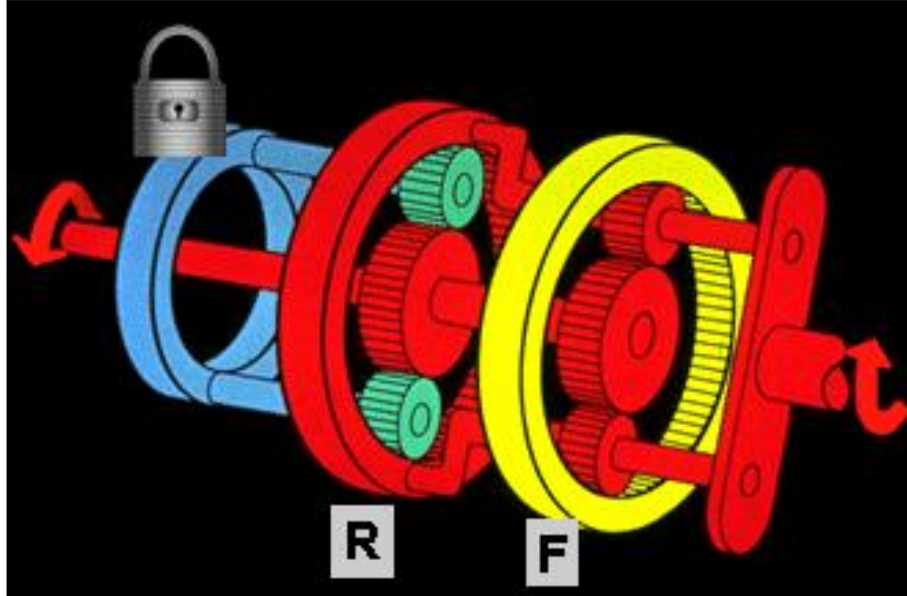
Engranajes en acoplamiento de reversa. (Caterpillar, 2012)
